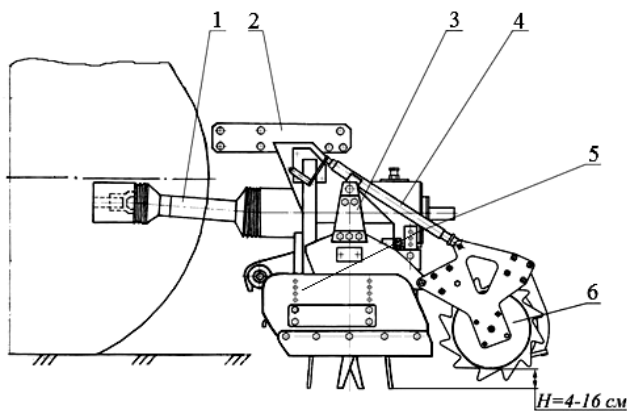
Схема почвообрабатывающей машины с активными рабочими органами:
